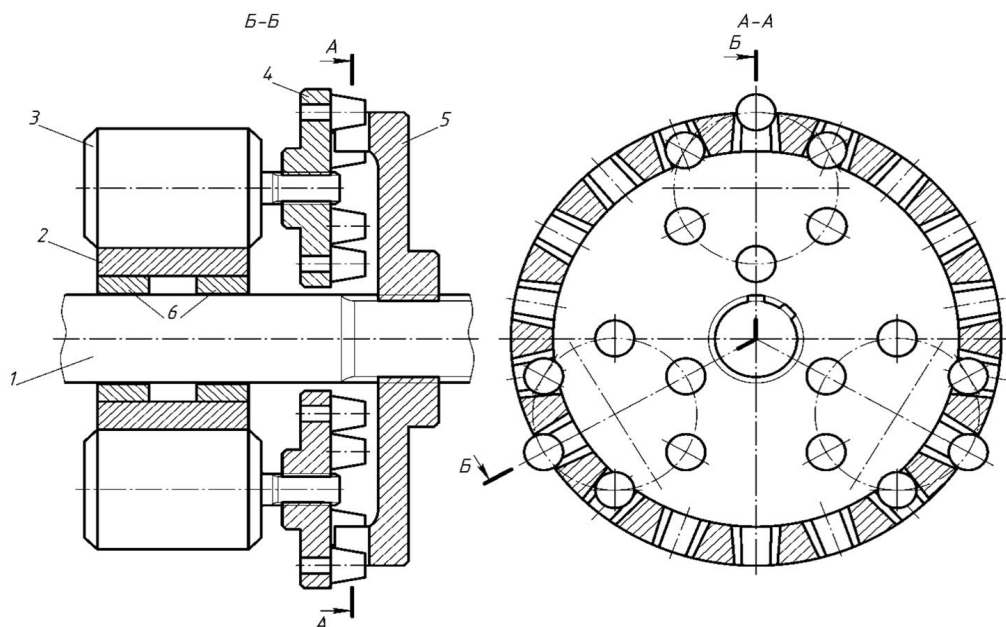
Компоновочная схема тягового привода с опорно-осевым подвешиванием пакета тяговых двигателей.
